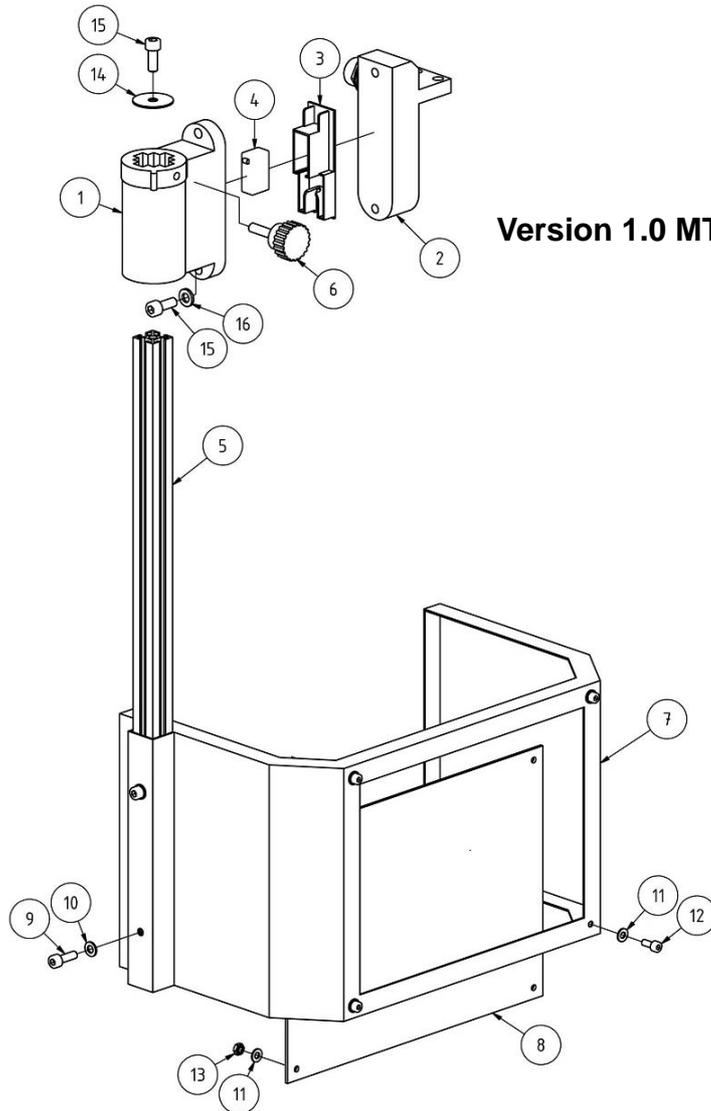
Fräsfutterschutz - Milling chuck protection
